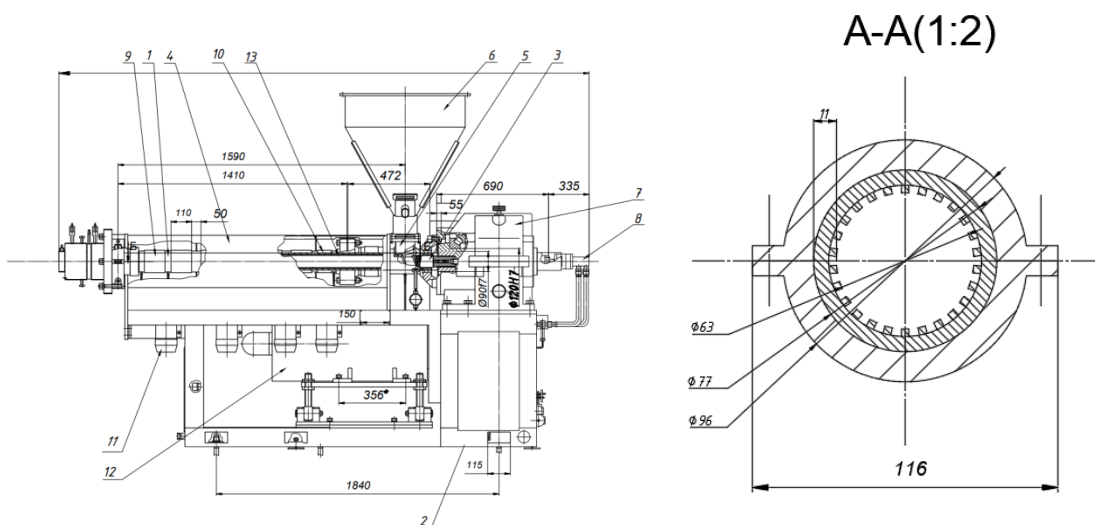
Загальний вид екструдера з удосконаленою конструкцією корпусу зі сталевих пластин:
